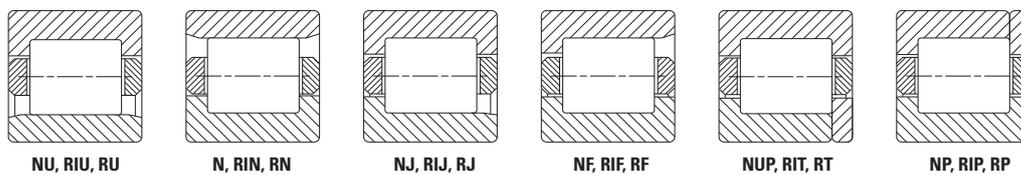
Typen der Standardzylinderrollenlager metrisch/Zoll.
